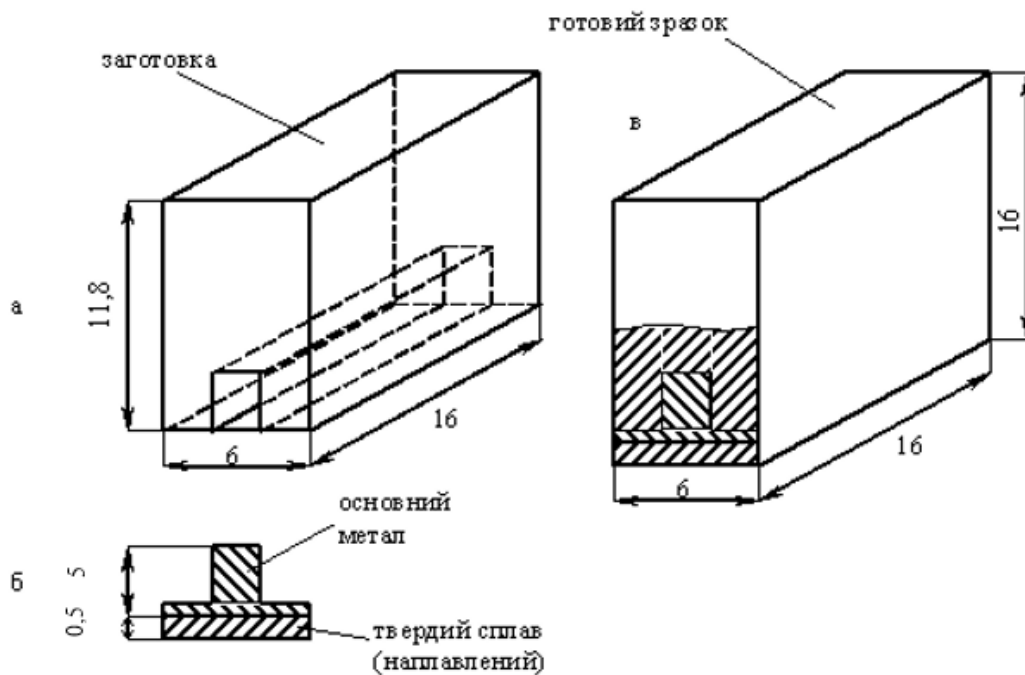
Конструктивні розміри зразків для дослідження на зносостійкість: а – прямокутна заготовка; б – Т-подібна вставка з основним і наплавленим металом; в – готовий зразок
